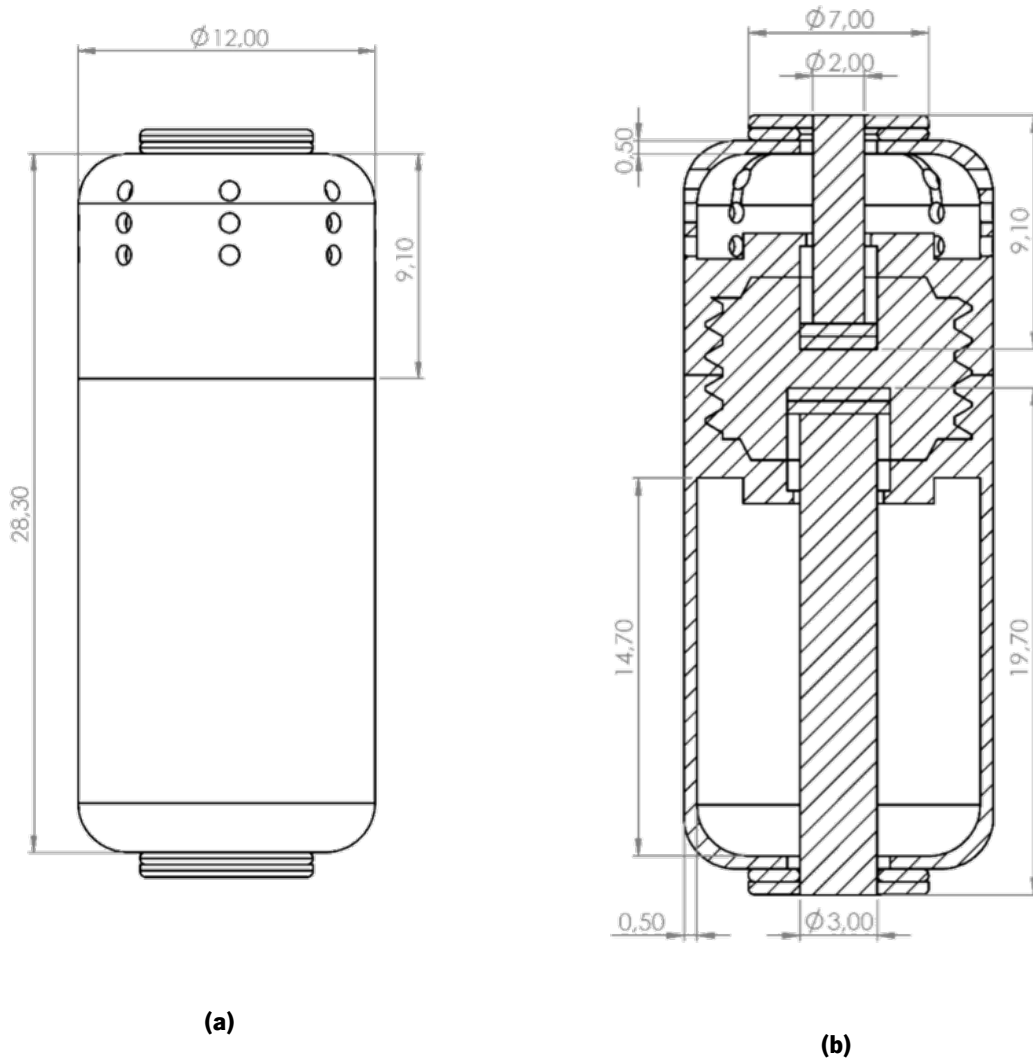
Design* CAD e dimensões (mm) do corpo da cápsula ingerível 1.0 (Disco 4-3 mm): a) vista lateral, b) vista em corte.
